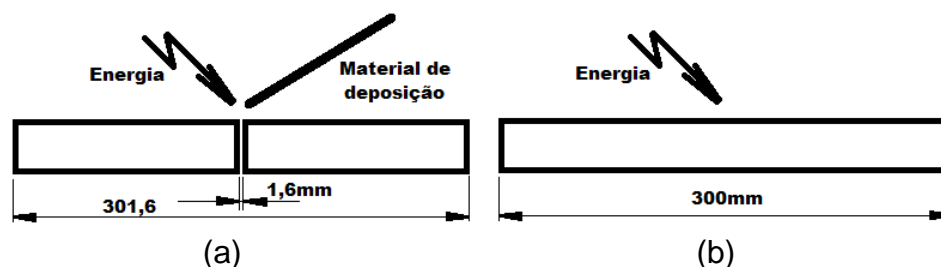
Desenho esquemático dos corpos de prova e sua montagem para a soldagem com (a) e sem metal de adição (b).
